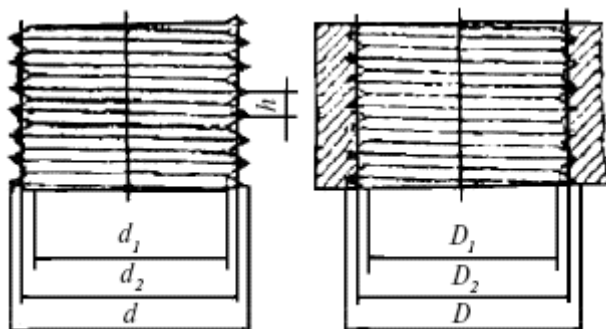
Разрез и профиль резьбы: а – винта; б – гайки
